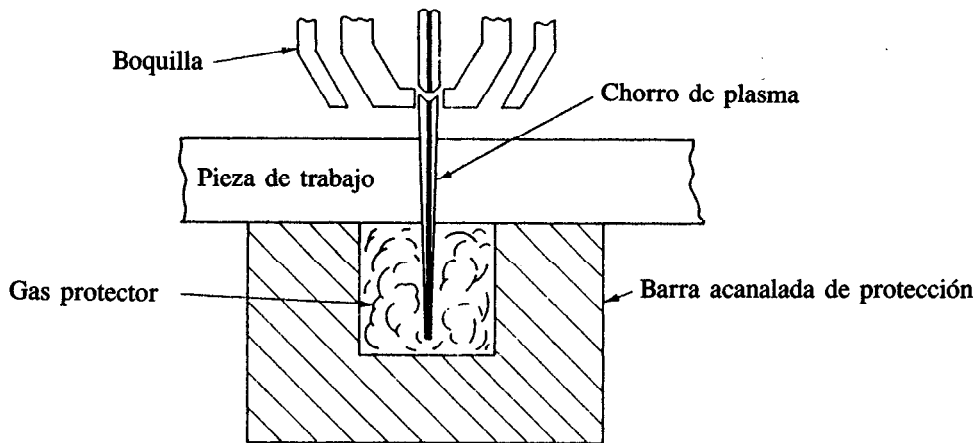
Uso de una barra acanalada de protección en la soldadura de arco de plasma.
